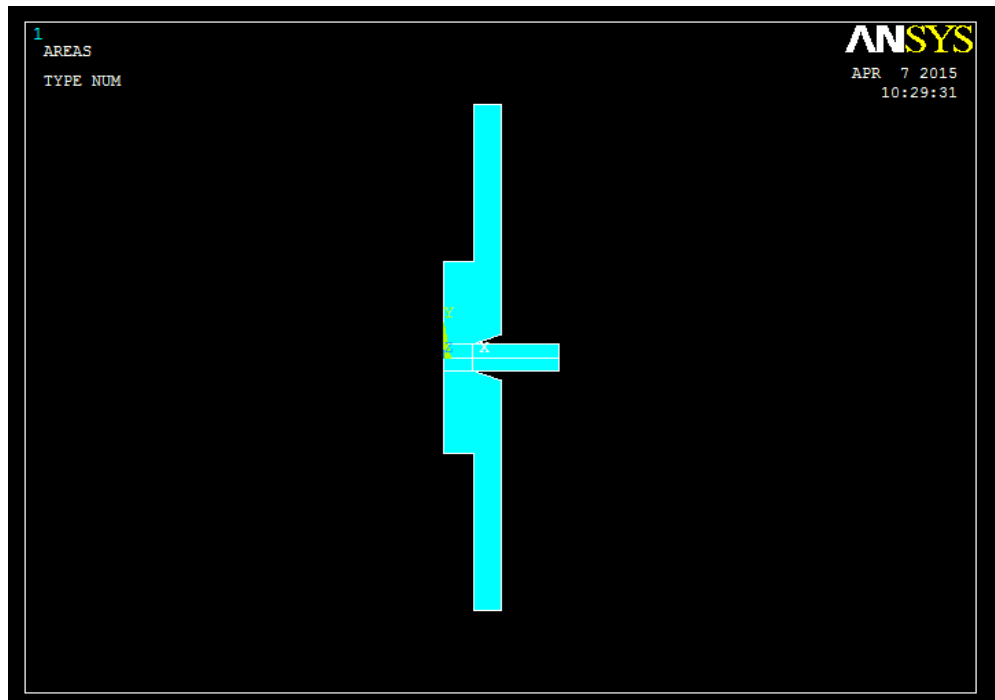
Géométrie du dispositif de soudage par point (électrodes/plaques)
